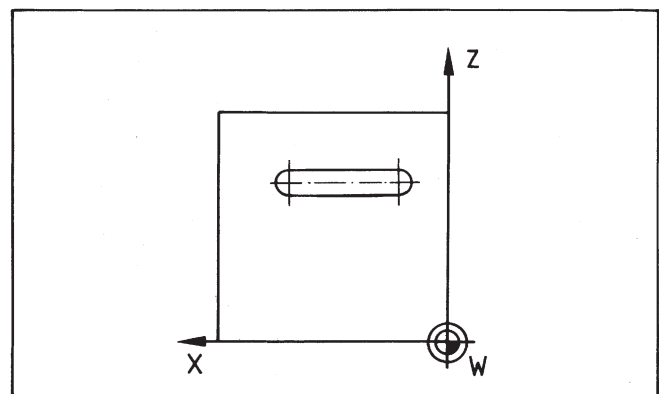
Wahl des Werkstücknullpunkts bei der Universal-Werkzeugfräsmaschine MF2
